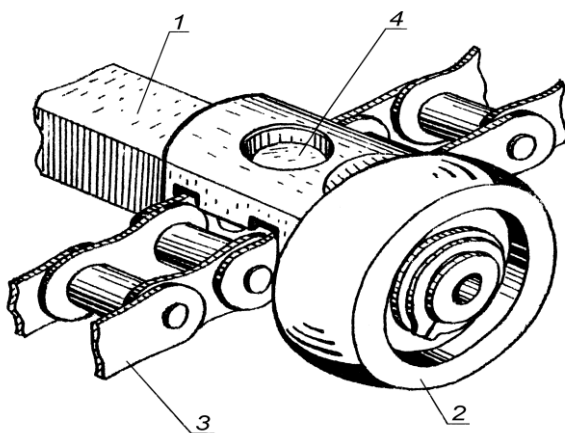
Механизм прессующий: 1 – планка (скалка); 2 – роликовая опора; 3 – цепь; 4 – фиксатор.
